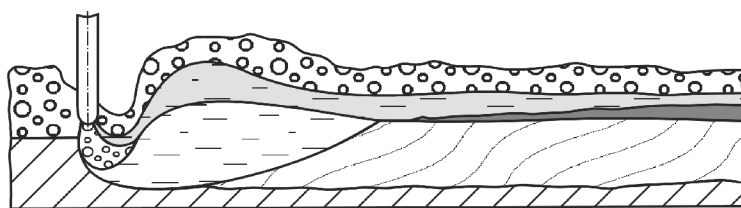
Новая схема процесса сварки под флюсом [6]
